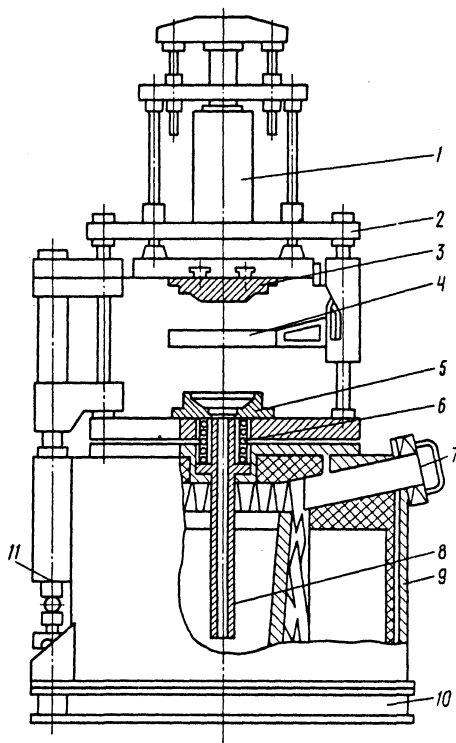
Схема машины для литья под низким давлением мод. 83105: 1 - гидропривод вертикальных перемещений кокиля; 2 - кокильный агрегат; 3 - подвижная полуформа; 4 - приемник отливок; 5 - неподвижная полуформа; 6 - нагреватель устья металлопровода; 7 - лок заливки сплава в камеру; 8 - металлопровод; 9 - заливочная камера; 10 - станина; 11 - гидропривод подъема кокильного агрегата
